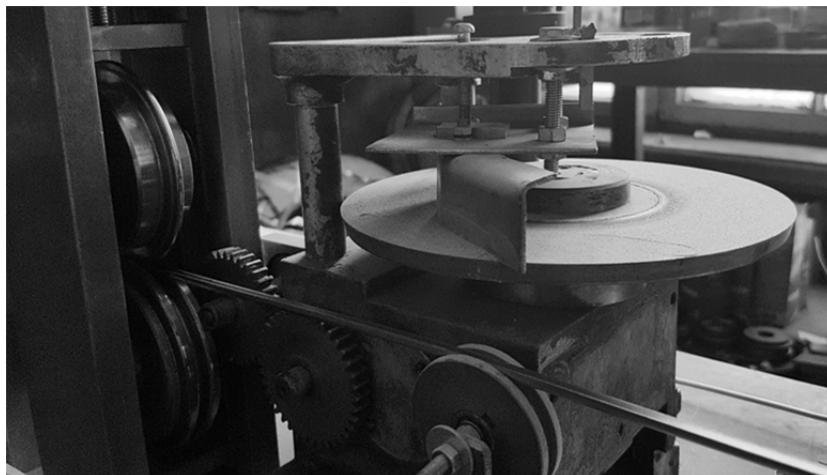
Тарельчатый дозатор лабораторного стана для заполнения заготовки шихтой.
